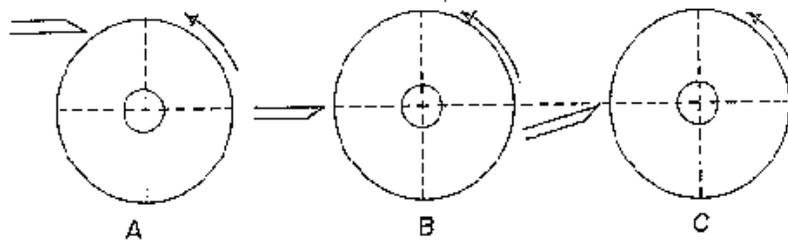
Tipos de Corte en Ensayos de Torneado
